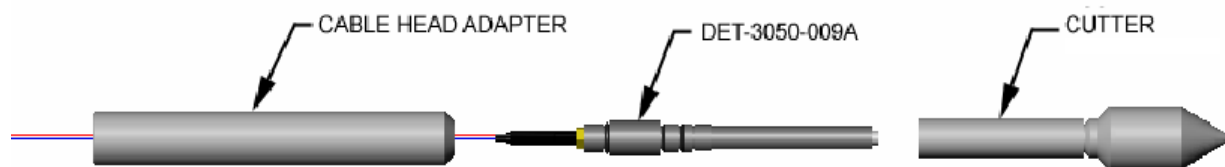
Méthode d'armement des outils de coupe Coil Tubing Cutter - Vue éclatée
